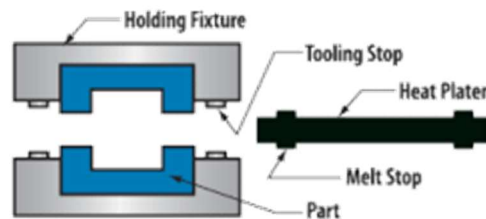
Partes del proceso de soldadura de plásticos mediante herramienta caliente por forwardtech.
